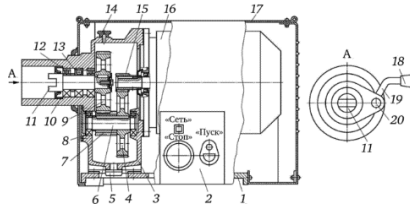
Привод ПМ: 1 — рама; 2 — пост управления; 3 — редуктор; 4, 9 — колесо зубчатое; 5 — пробка сливная; 6 — вал промежуточный; 7, 15 — шестерня; 8, 12 — шарикоподшипник; 10 — манжета; 11 — вал приводной; 13 — подшипник упорный; 14 — пробка-сапун; 16 — электродвигатель; 17 — кожух; 18 — рукоятка; 19 — кулачок; 20 — ось
